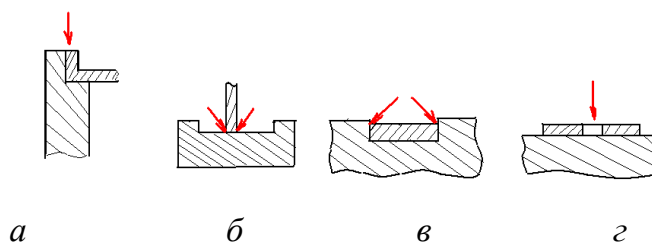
Сварные соединения деталей разной толщины:
